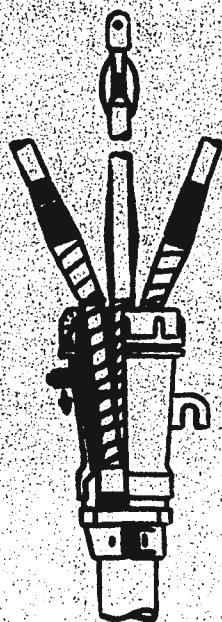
Disposición de los Conos de efluvios en un manguito terminal para interior y cable aislado con plástico.
